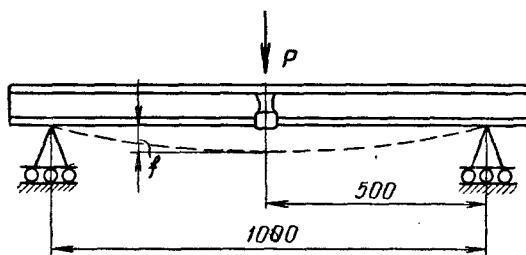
Испытание сварного стыка рельсов на статический излом.
